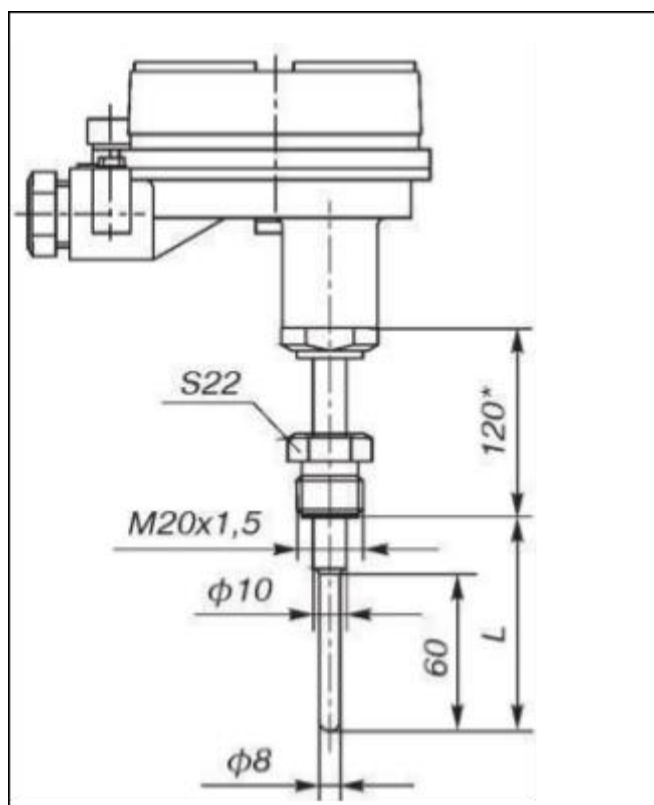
Габаритные и присоединительные размеры Метран–288
